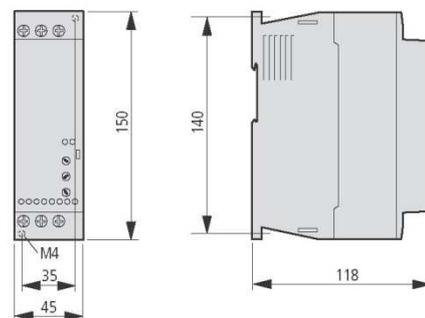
Esquema de dimensiones DS7: 16 a 32 A
